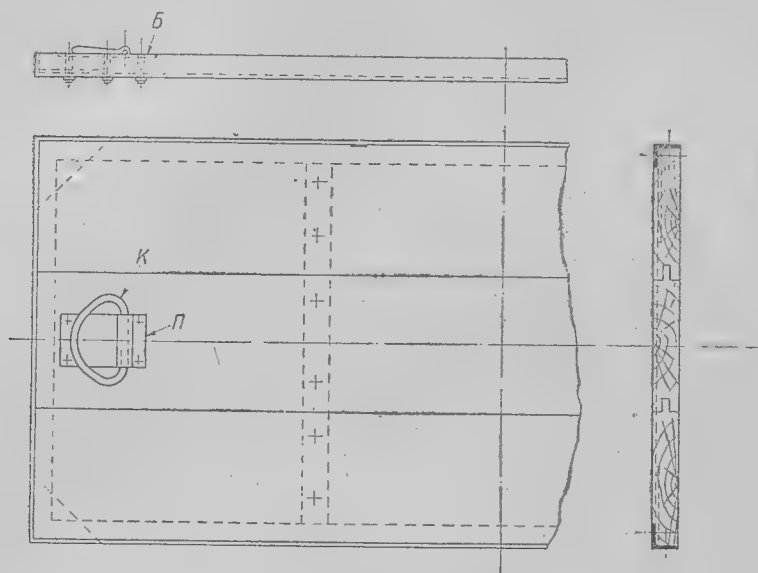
Крышка люка: К — кольцо люка, П — металлическая планка для крепления кольца и крышка люка, Б — болты, крепящие планку.
